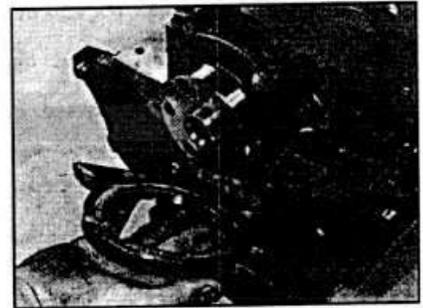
С.62. Установка крышки левого уплотнительного кольца коленчатого вала.
